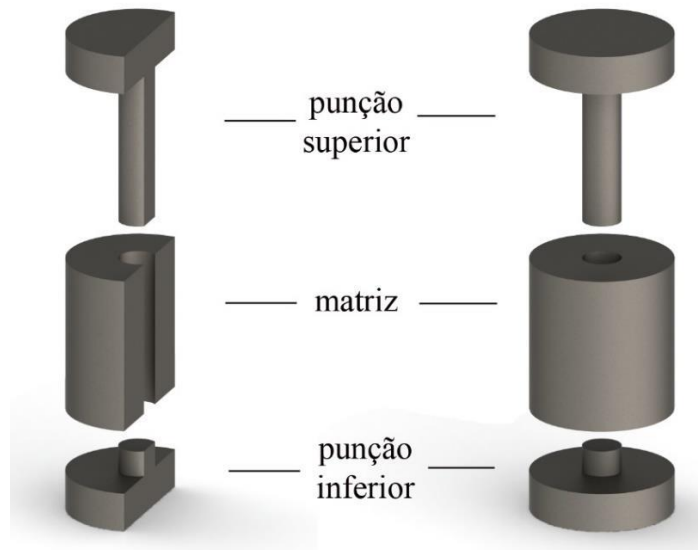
Molde cilíndrico utilizado na etapa de compactação
